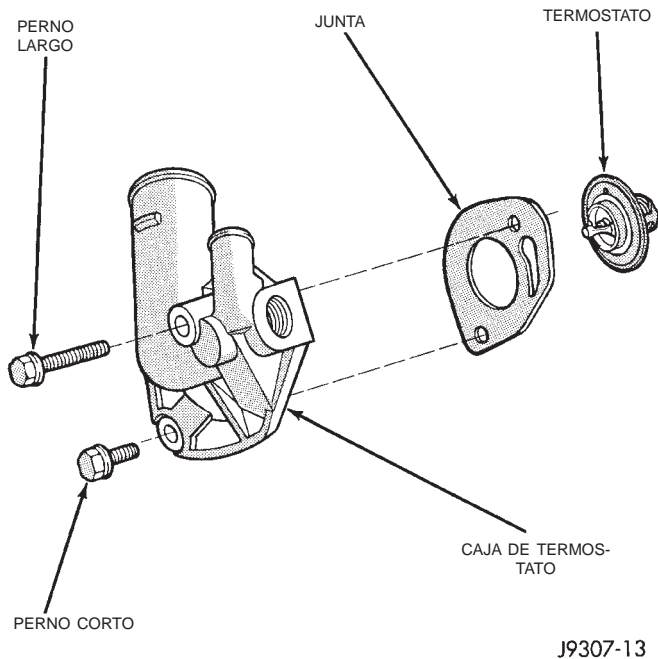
Desmontaje e instalación de termostato—Motor de 4.0L
